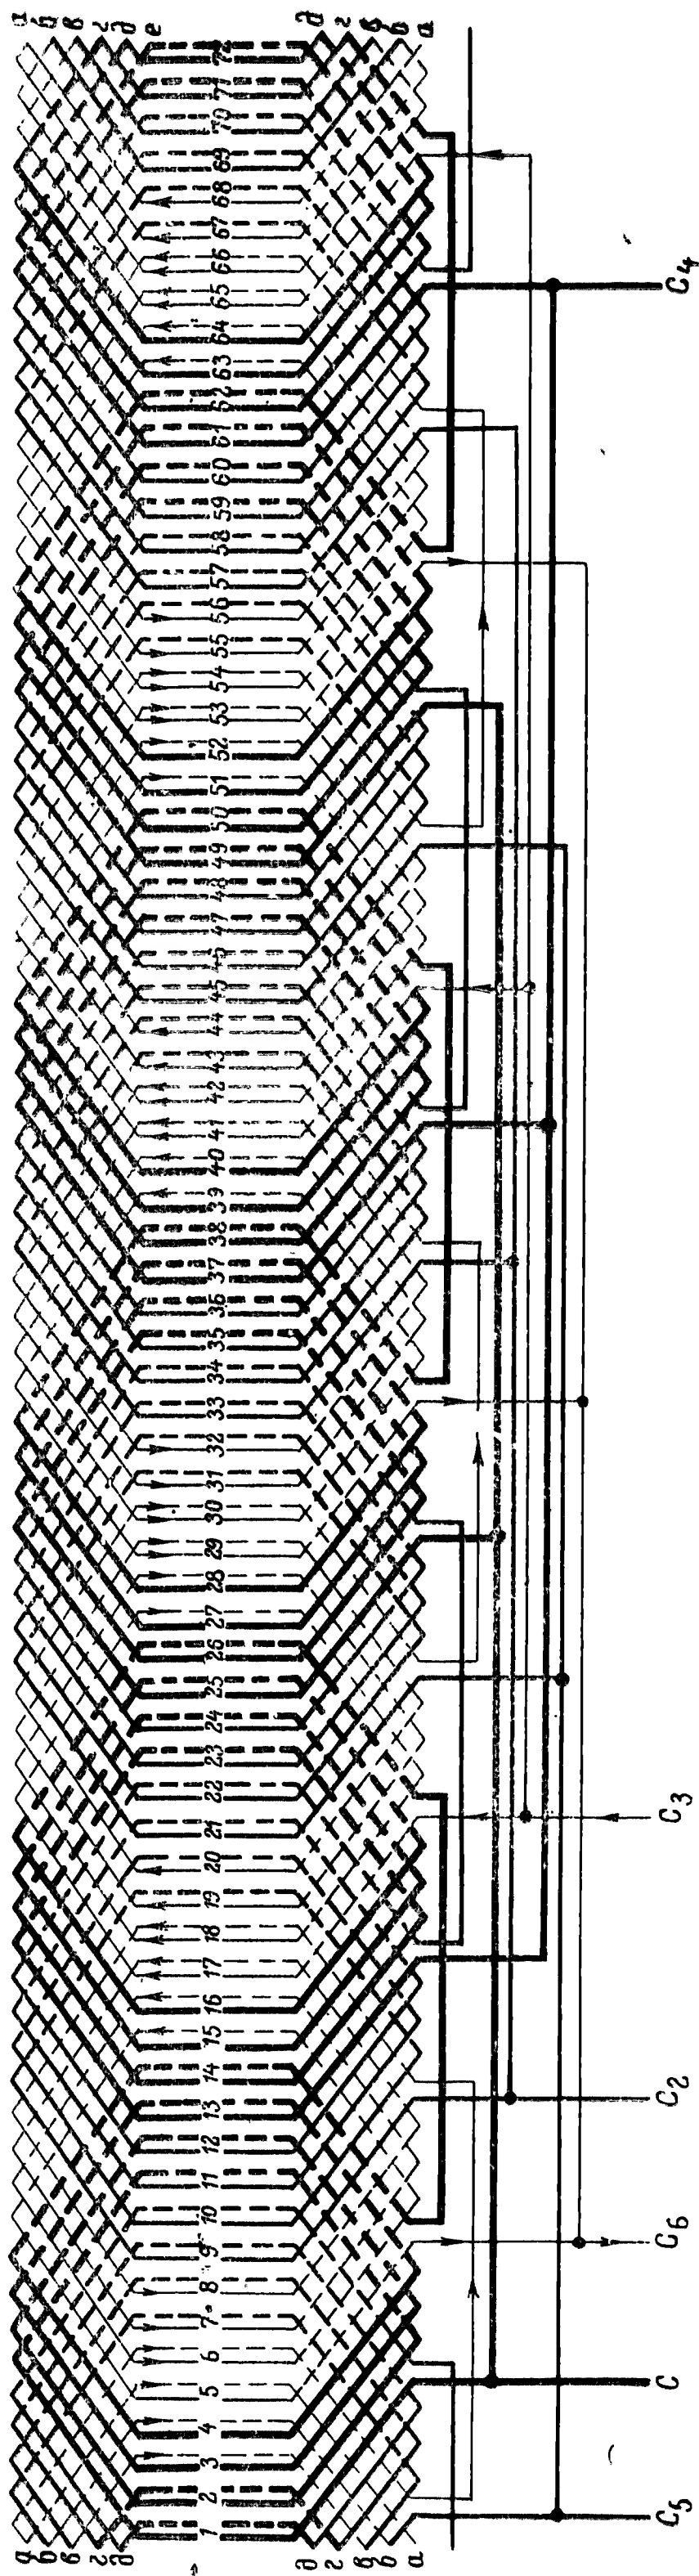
Развернутая схема двухслойной статорной обмотки при $2p=6$; $z=72$; $q=4$; $y=1-11$; $a=3$. Для электродвигателей на напряжение 500 в выводить только три конца — C_1 , C_2 , C_3 . Для образования нулевой точки концы фаз C_4 , C_5 , C_6 соединить между собой.
